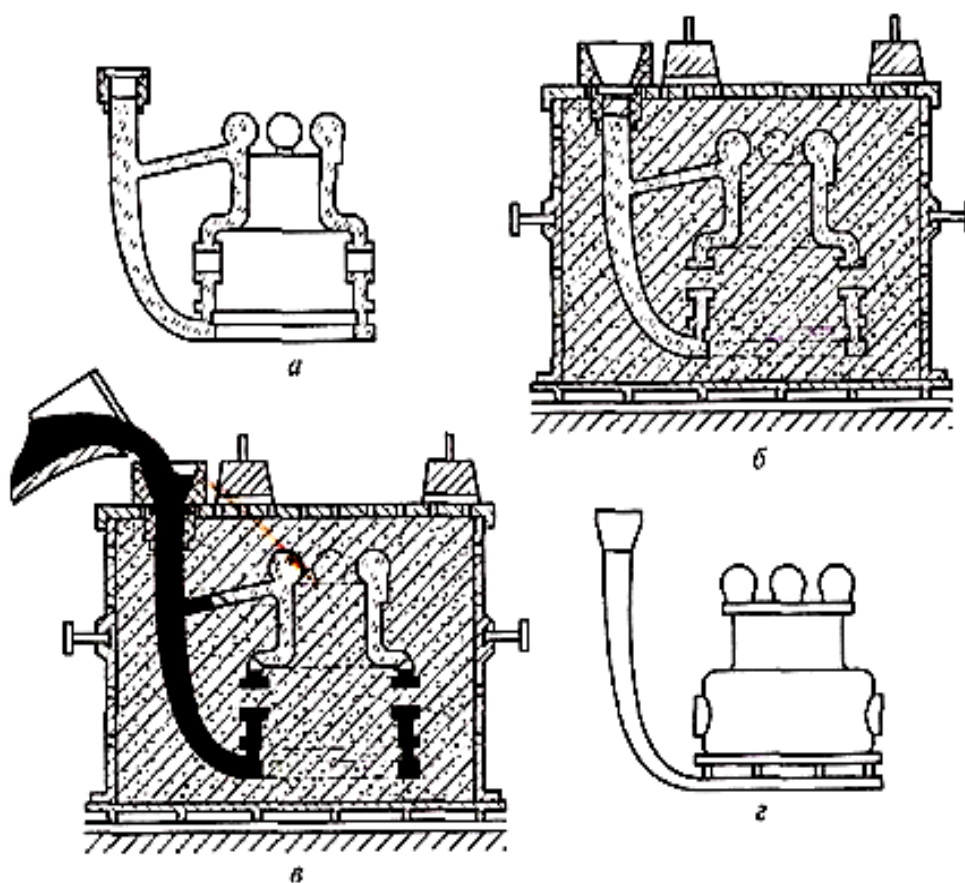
Схема изготовления отливки по газифицируемой модели: а - пенополистироловая модель отливки; б — форма, подготовленная к заливке;
